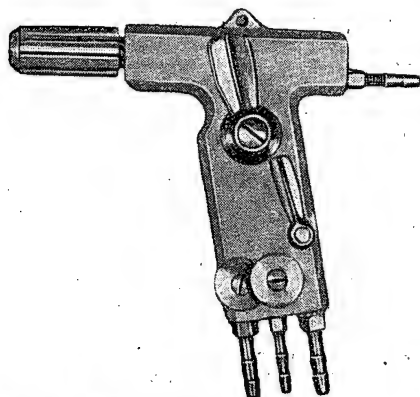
Металлизатор для распыления проволоки из цинка и алюминия.
